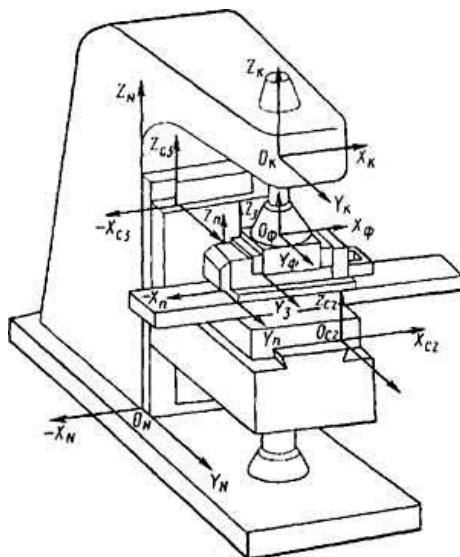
Траектории главного и вспомогательных движений вертикально-фрезерного станка 6P12
